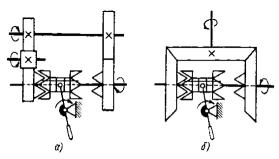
Реверсивные механизмы: а – цилиндрический; б – конический
